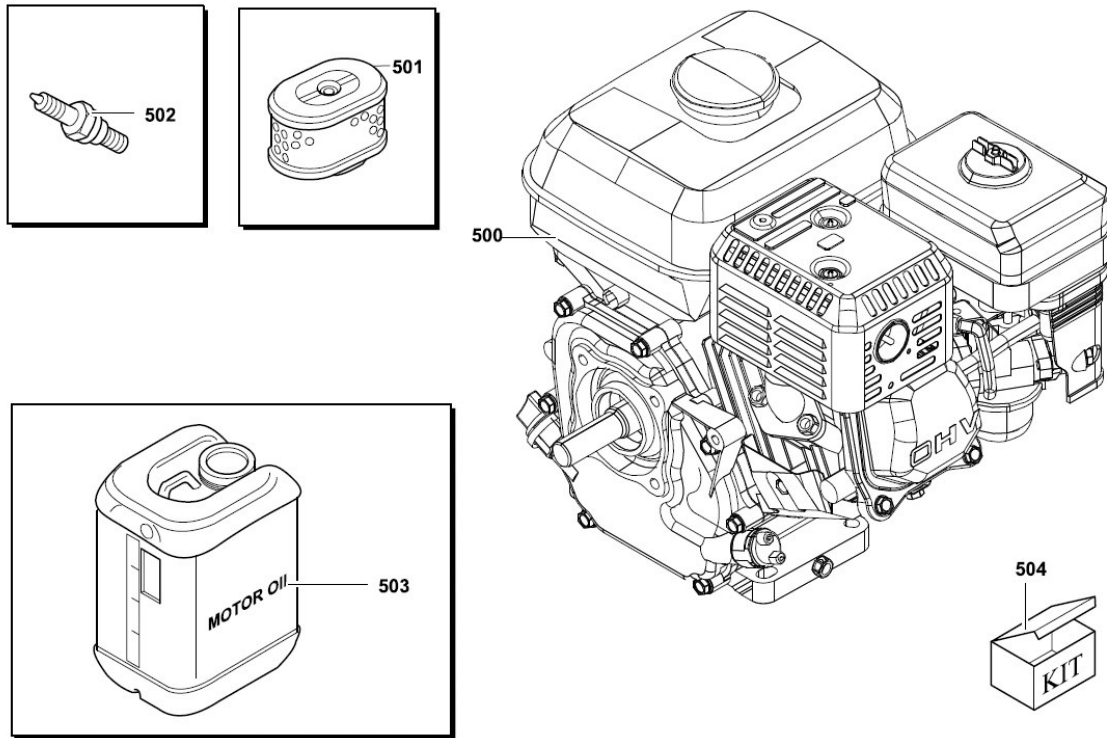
Ersatzteilzeichnung 3 - PG 320 SR
